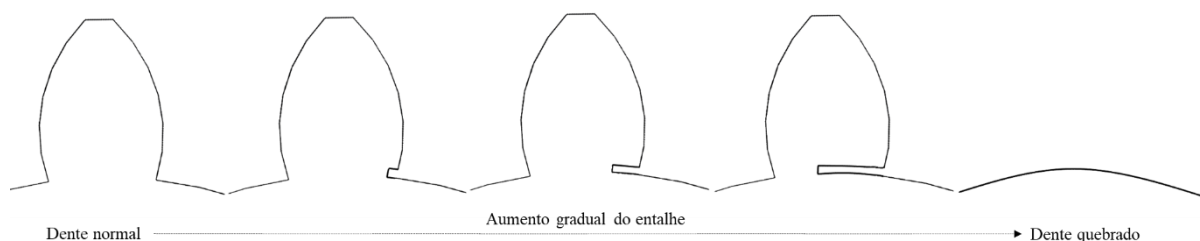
Dimensões do entalhe ao longo da face do dente de engrenagem.
